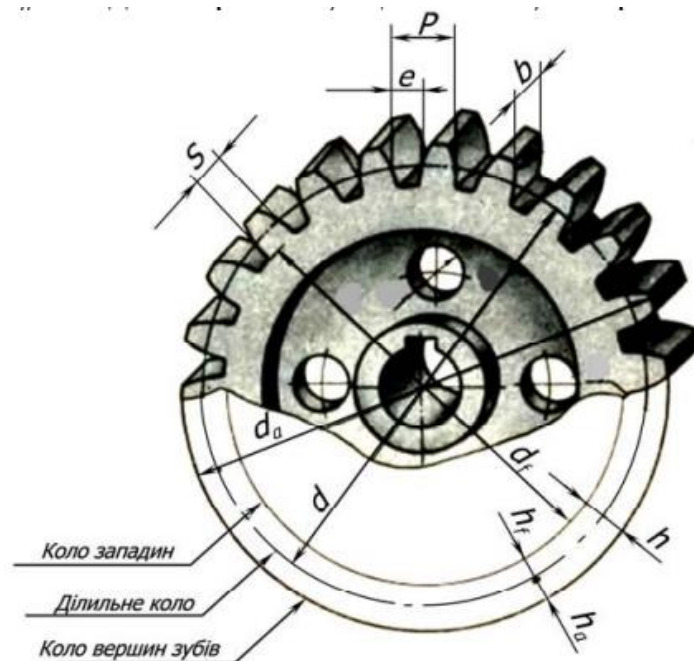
Основні параметри циліндричного зубчастого колеса
